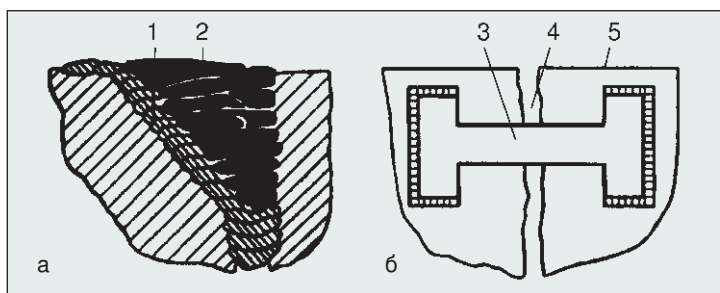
Восстановление изложниц с продольными трещинами: а — заварка трещины внутри; б — постановка анкера (1 — облицовка; 2 — наплавка; 3 — анкер; 4 — трещина; 5 — торец изложницы)
